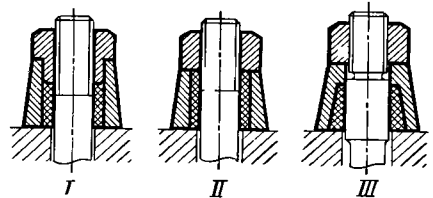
Стопорение пластмассовыми втулками, заключенными в корпуса
